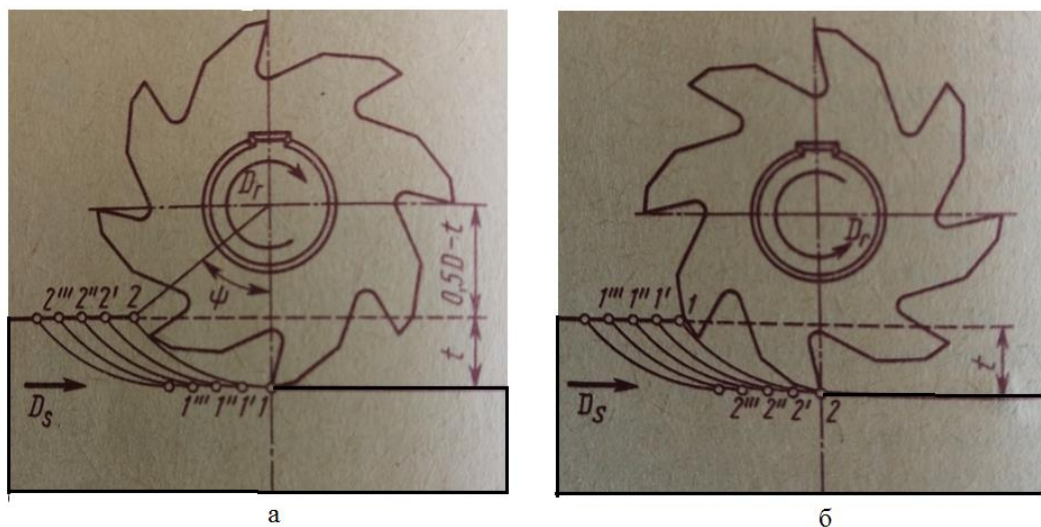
Зустрічне фрезерування (а) і попутне фрезерування (б)
